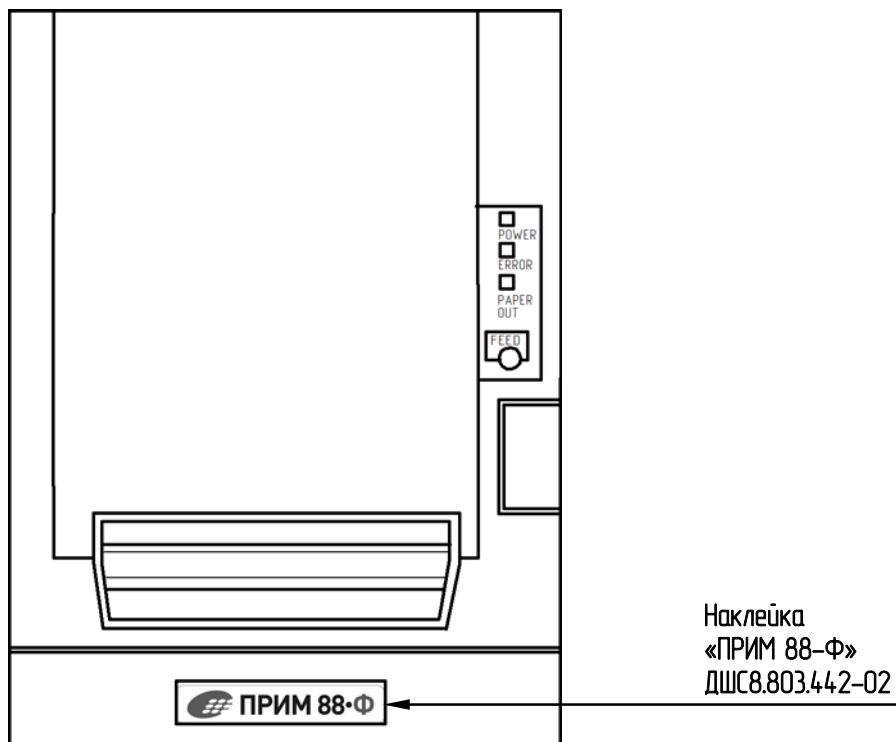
Установка наклейки «ПРИМ 88-Ф» (вид сверху)
